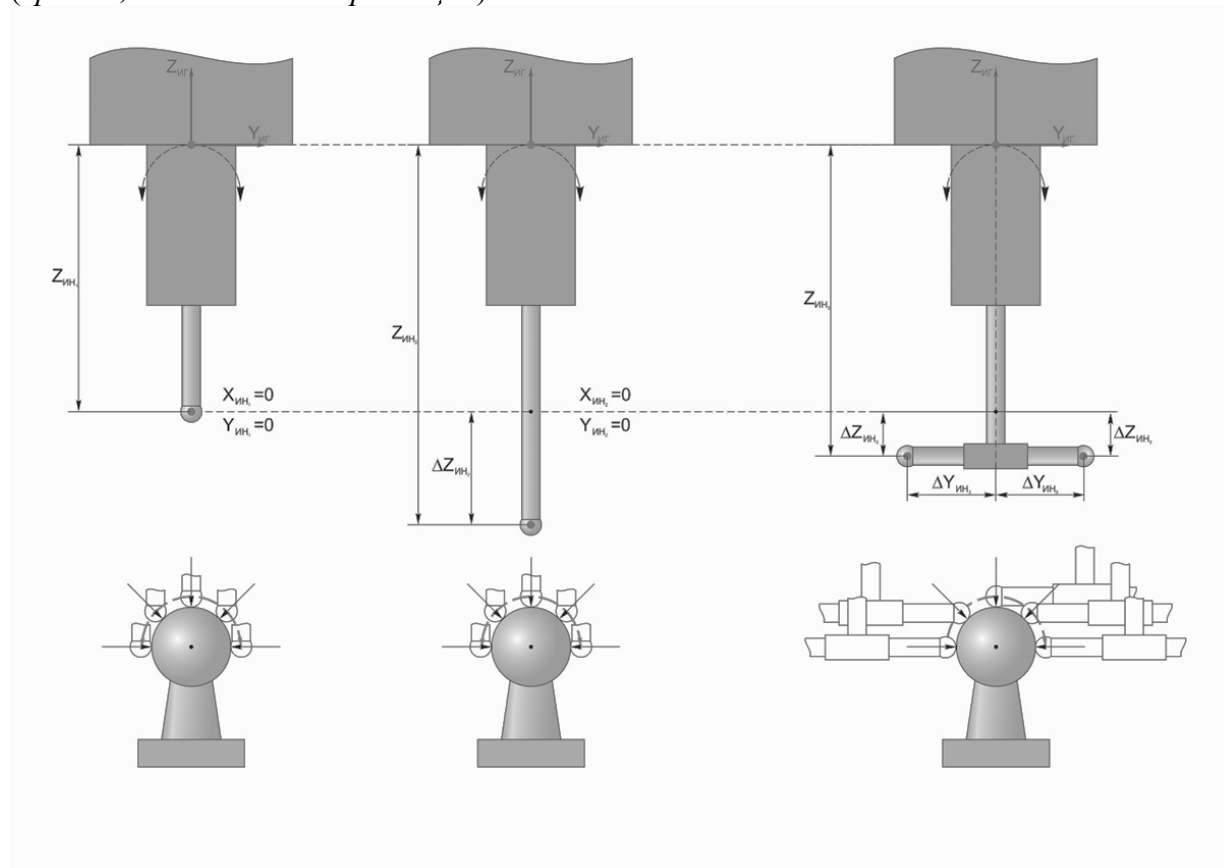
Пример калибровки ИН различных типоразмеров и конструкций
